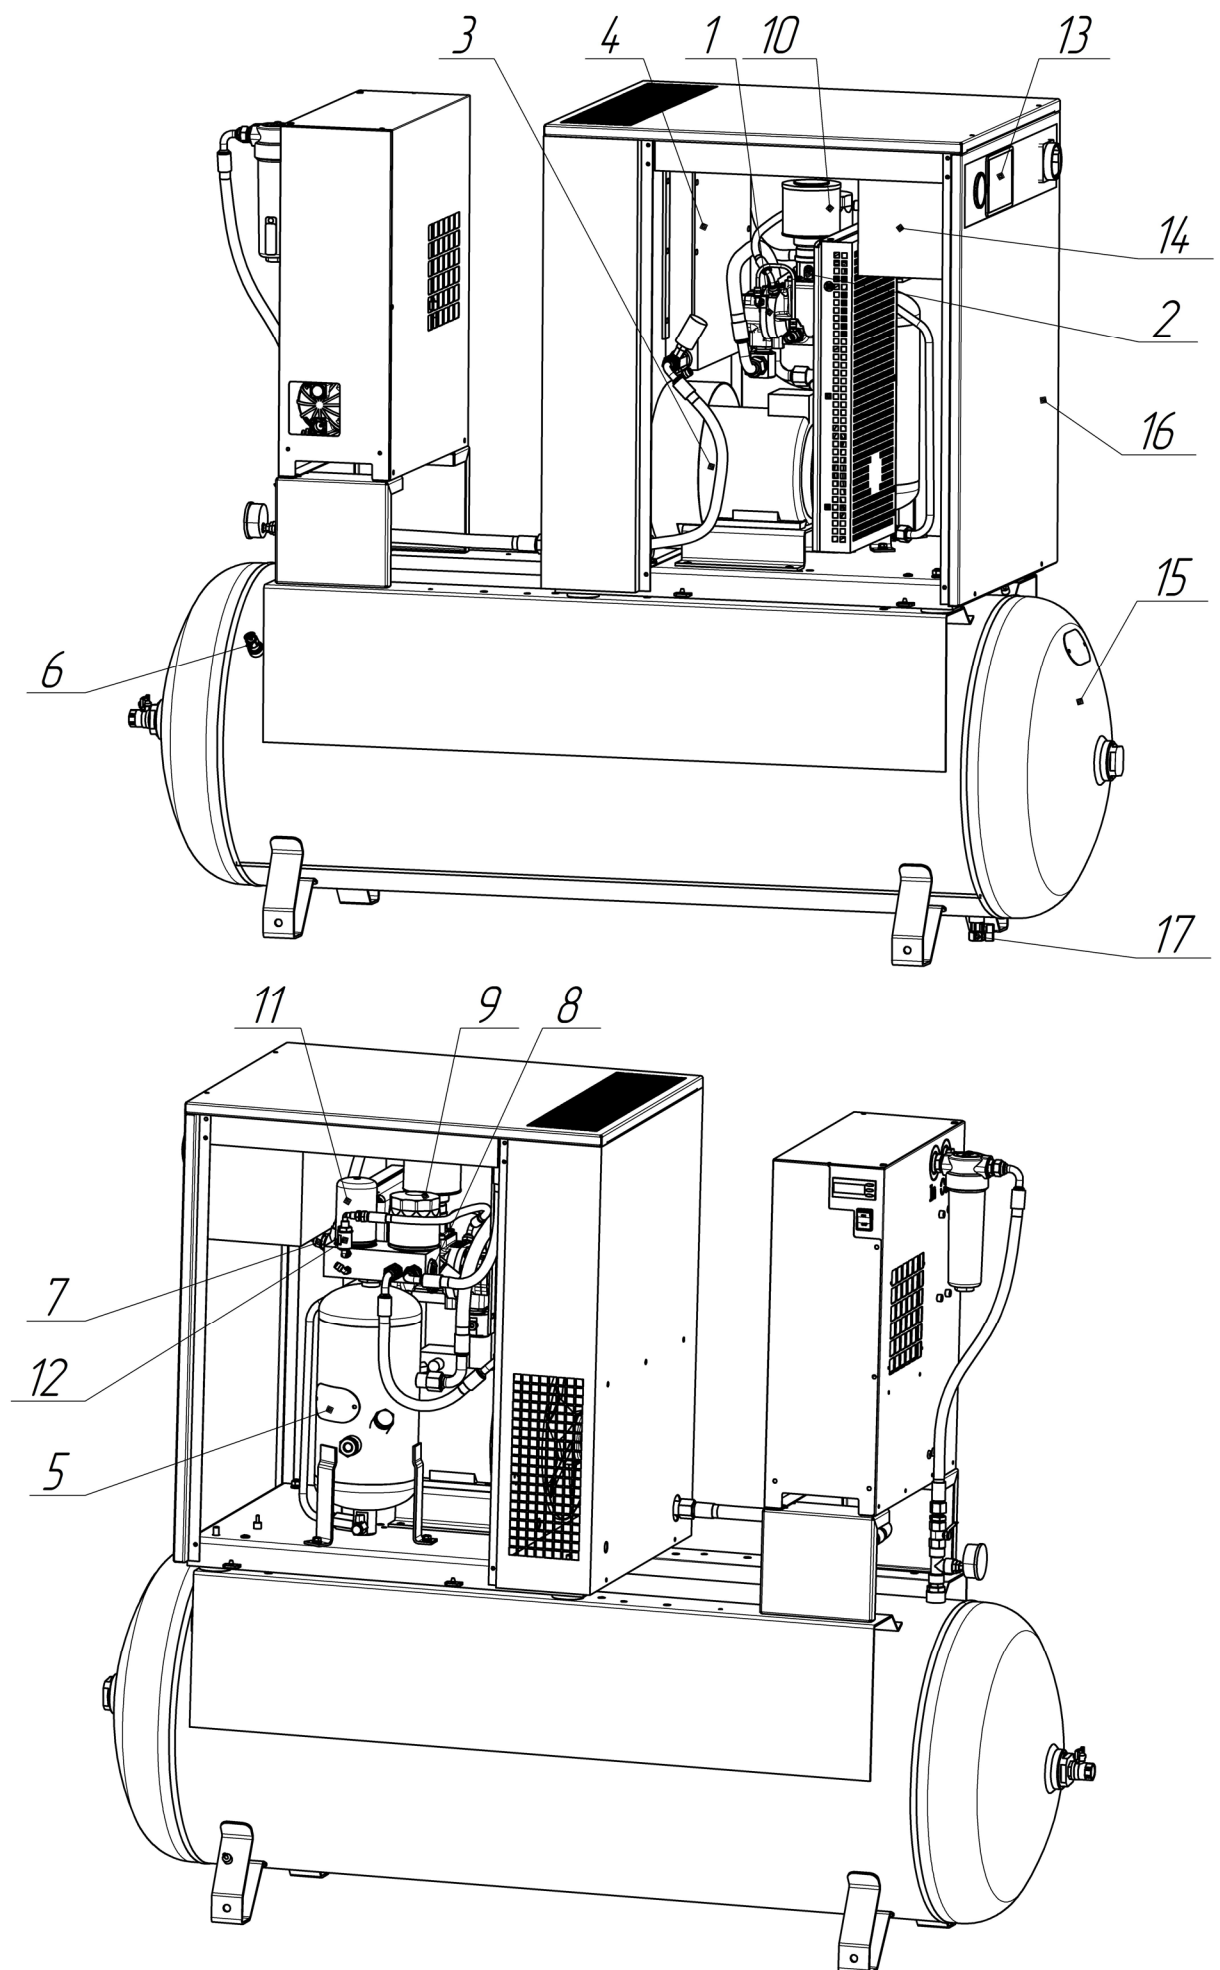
Общий вид компрессорной установки BK5(7, 10)E-...-500(Д)
